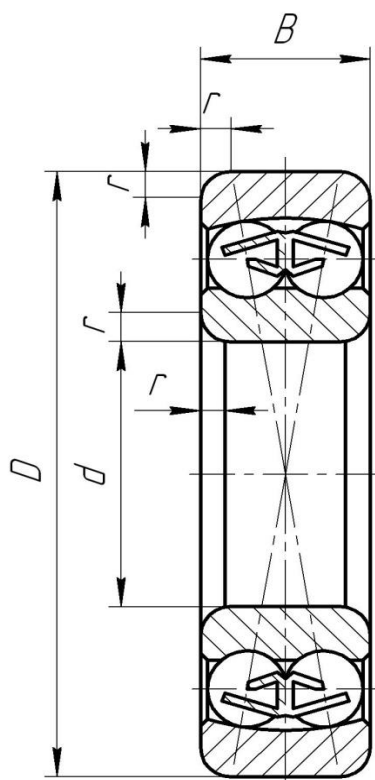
Подшипник радиальный сферический, двухрядный
